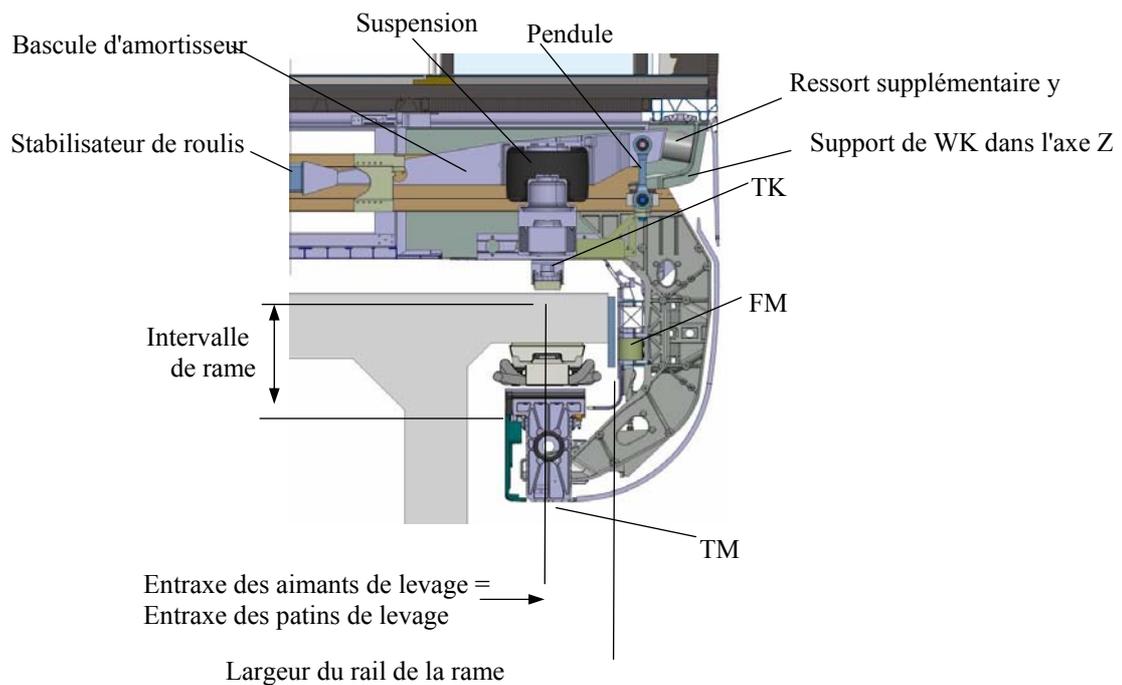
Vue latérale et vue transversale (schéma de principe)
